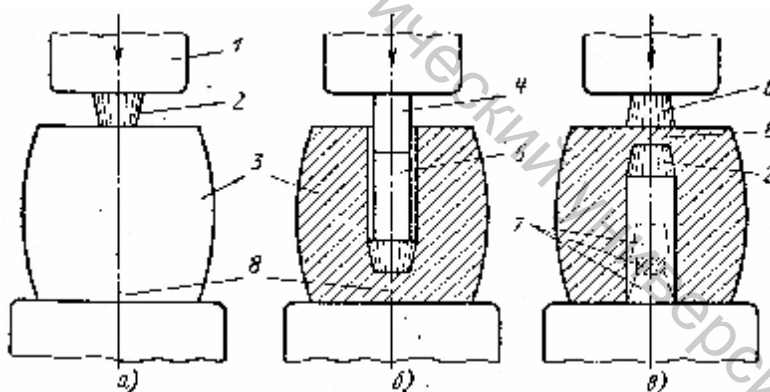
Прошивка без подкладного кольца: а-в- этапы прошивки, 1-верхний боек, 2-основной прошивень, 3- заготовка, 4,5- надставки, 6- прорезной прошивень, 7- прошивни и выдра после прошивки, 8- прибыльная сторона слитка
